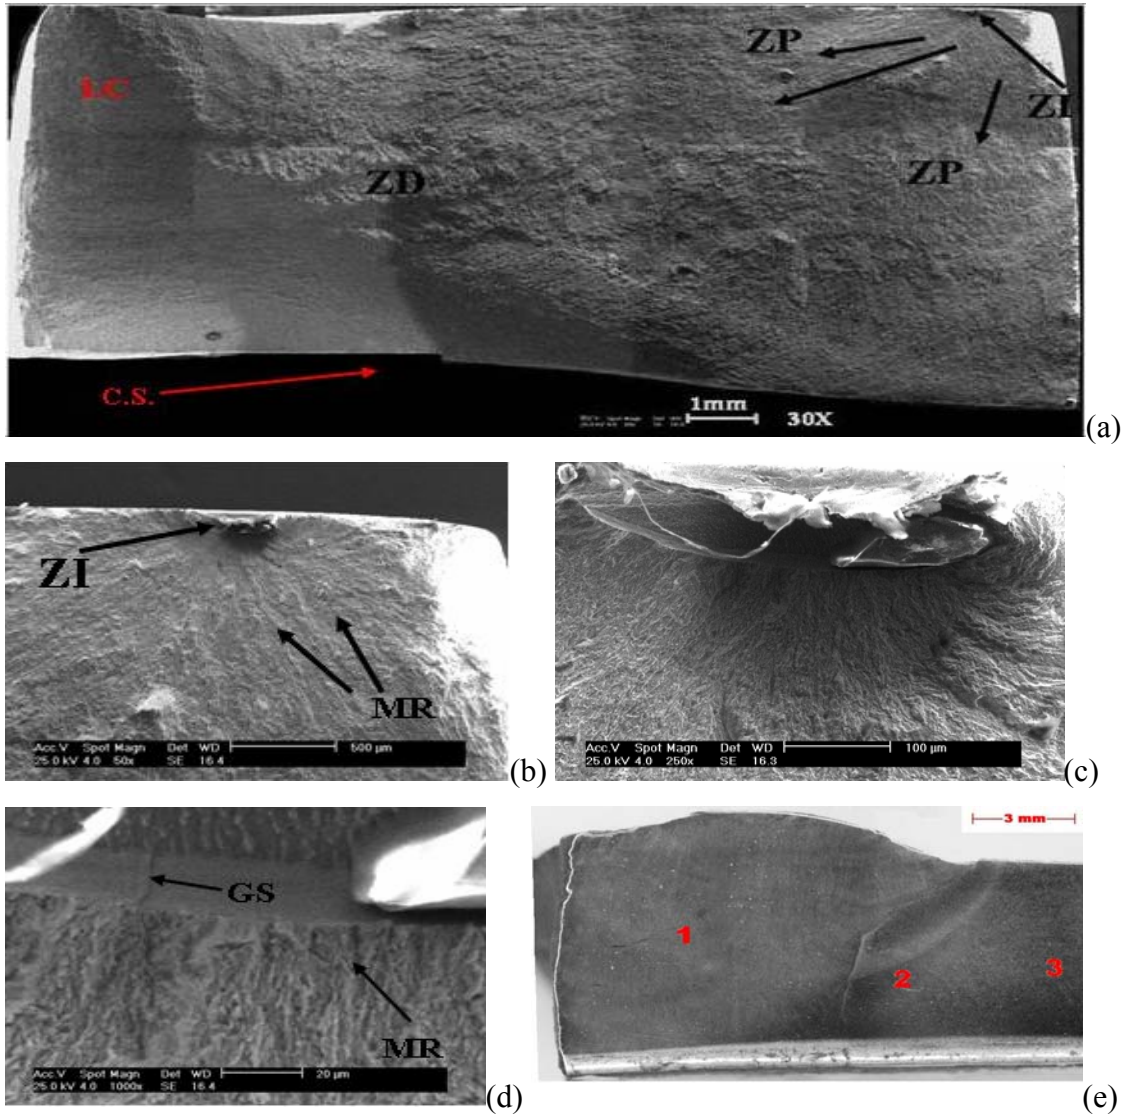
Fotomacrografía y fotomicrografías correspondientes a la junta soldada identificada como 19 sometida a fatiga uniaxial a 360 MPa, (a) Superficie de fractura [30X]; (b) Detalle del inicio de grieta [50X]; (c) Detalle a [250X]; (d) Detalle a [1000X]; (e) Lateral mostrando: 1-Cordón, 2-Z.A.C y 3- M.B.
